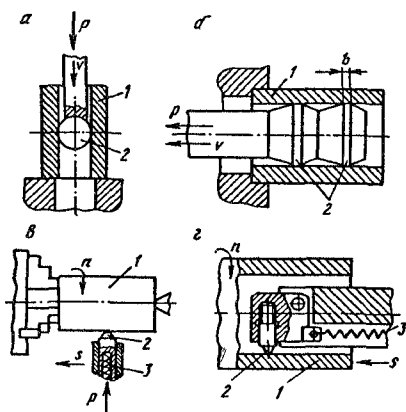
Схемы обработки способами ППД со скольжением инструментов: 1 — заготовка; 2 — инструмент; 3 — пружина
